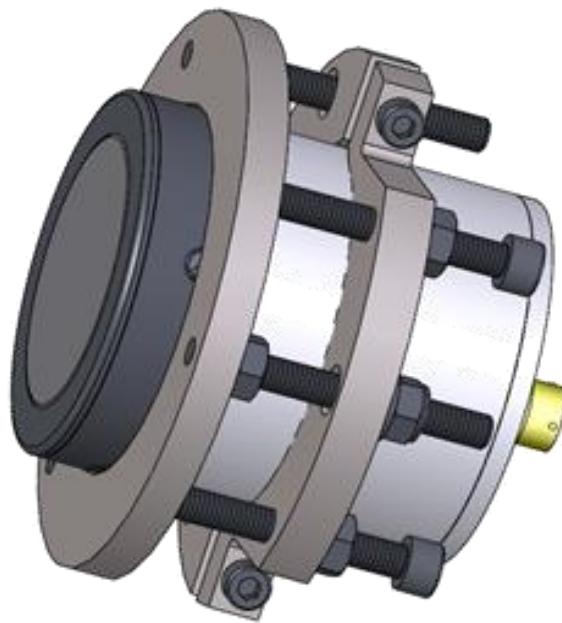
Anel de Aperto Ajustável (0033) Instalado na Placa de Fixação (0021) e Hydro-Mix
